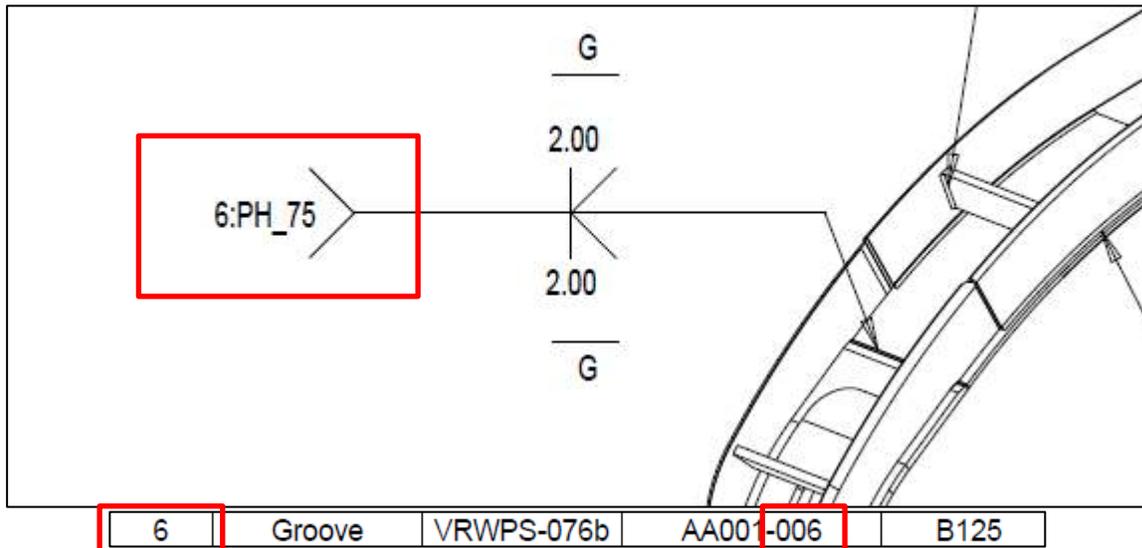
Ejemplo de No. de soldadura en Assembly Drawing
